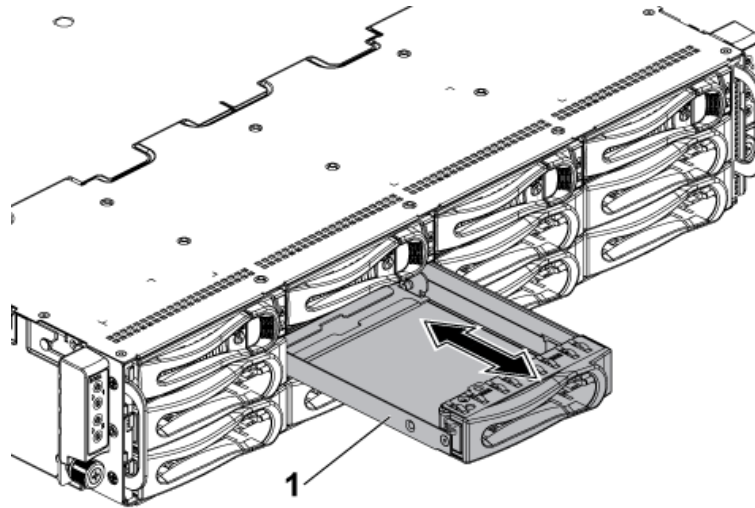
Entfernen oder Einsetzen einer 3,5-Zoll-Festplatten-Platzhalterkarte
